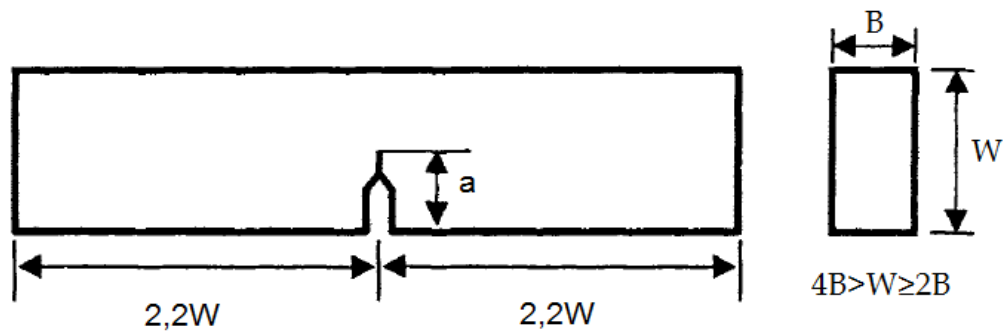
Dimensiones de probeta del ensayo a fractura.
